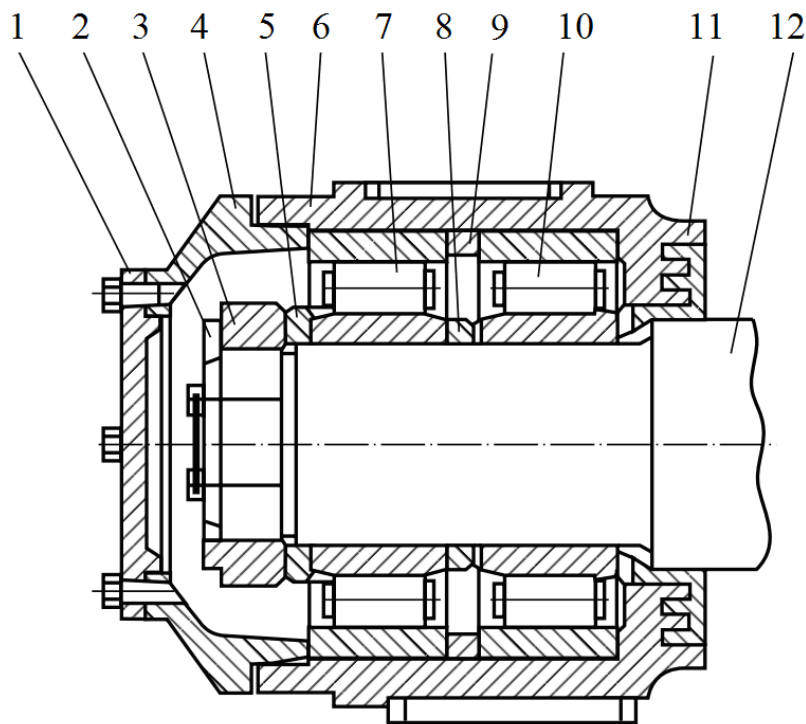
Букса з двома циліндричними роликовими підшипниками на гарячій посадці з кріпленням торцевою гайкою: 1 – кришка контрольна; 2 – пластина стопорна; 3 – гайка торцева; 4 – кришка крипильна; 5 – кільце упорне; 6 – корпус букси; 7, 10 – підшипники циліндричні; 8, 9 – кільця дистанційні; 11 – лабіринтне кільце; 12 – вісь колісної пари
